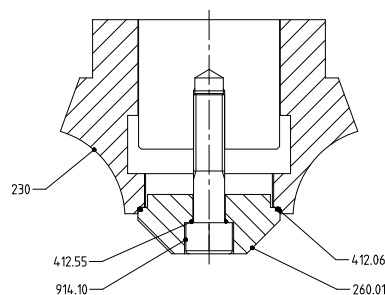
Крепление рабочего колеса М100х2 (для проточной части К 500-632, К 500-640)
